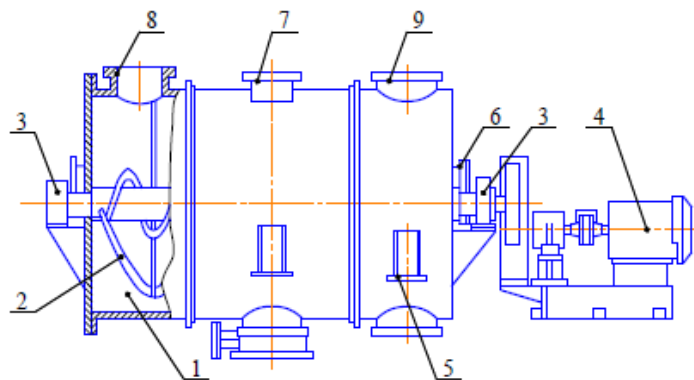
Змішувач стрічковий горизонтальний типу СЛН-10: 1 – корпус змішувача; 2 – стрічкова мішалка; 3 – опорні підшипники; 4 – привід змішувача; 5 – опорні лапи; 6 – люк для огляду; 7 – штуцер для вентиляції; 8, 9 – штуцери для завантаження матеріалу; 10 – штуцер для вивантаження матеріалу [1].
